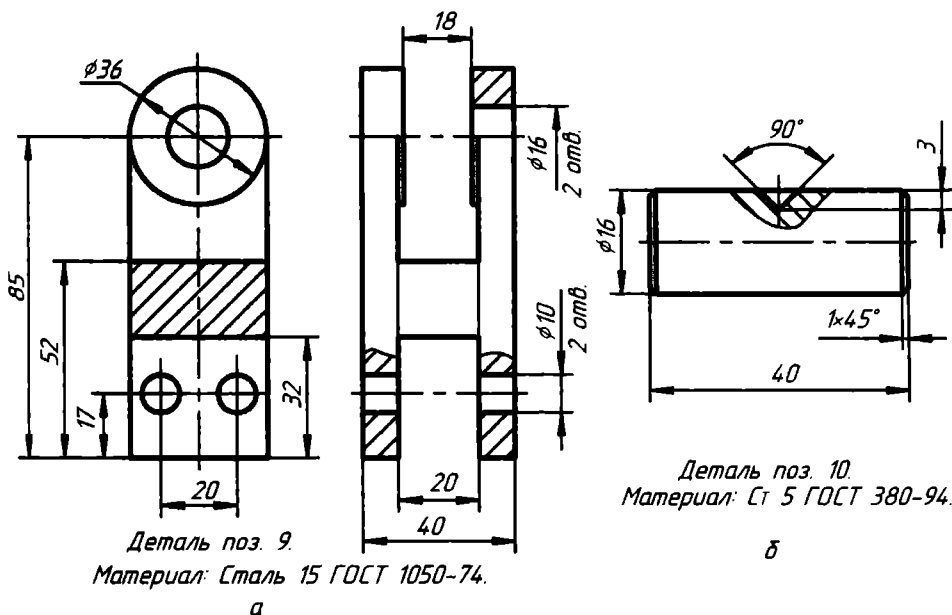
Чертежи: а — вилки; б — оси клапана
